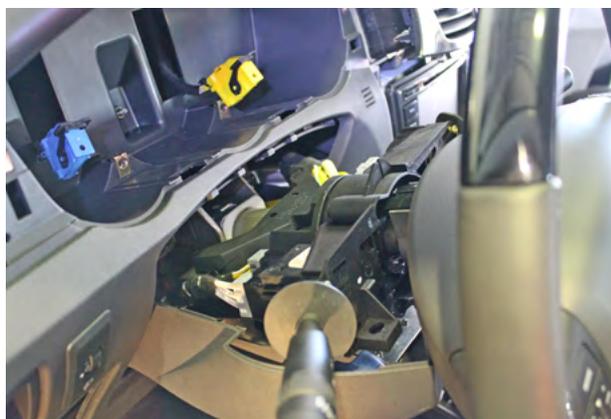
Верхняя часть кожуха рулевого вала снята
